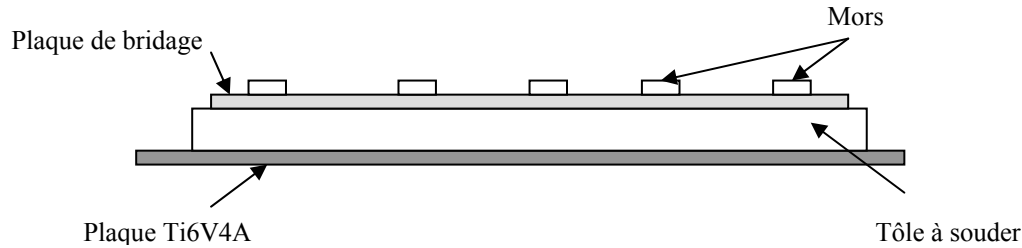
Dispositif de soudage vue en coupe longitudinale. La direction de soudage est parallèle à l'horizontale du schéma
